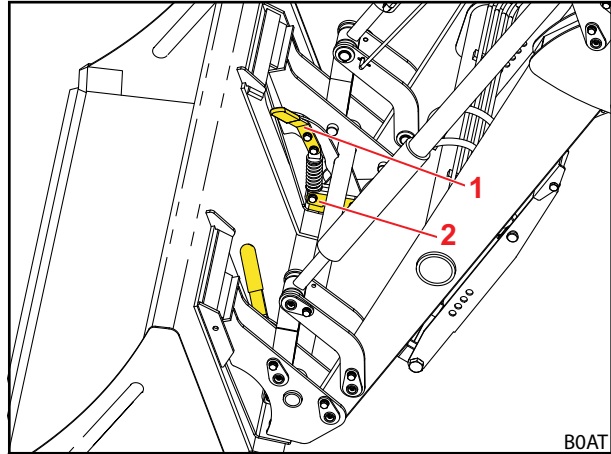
Mechanische Werkzeug-Verriegelung Skid-Steer (verriegelter Zustand mit Werkzeug)
